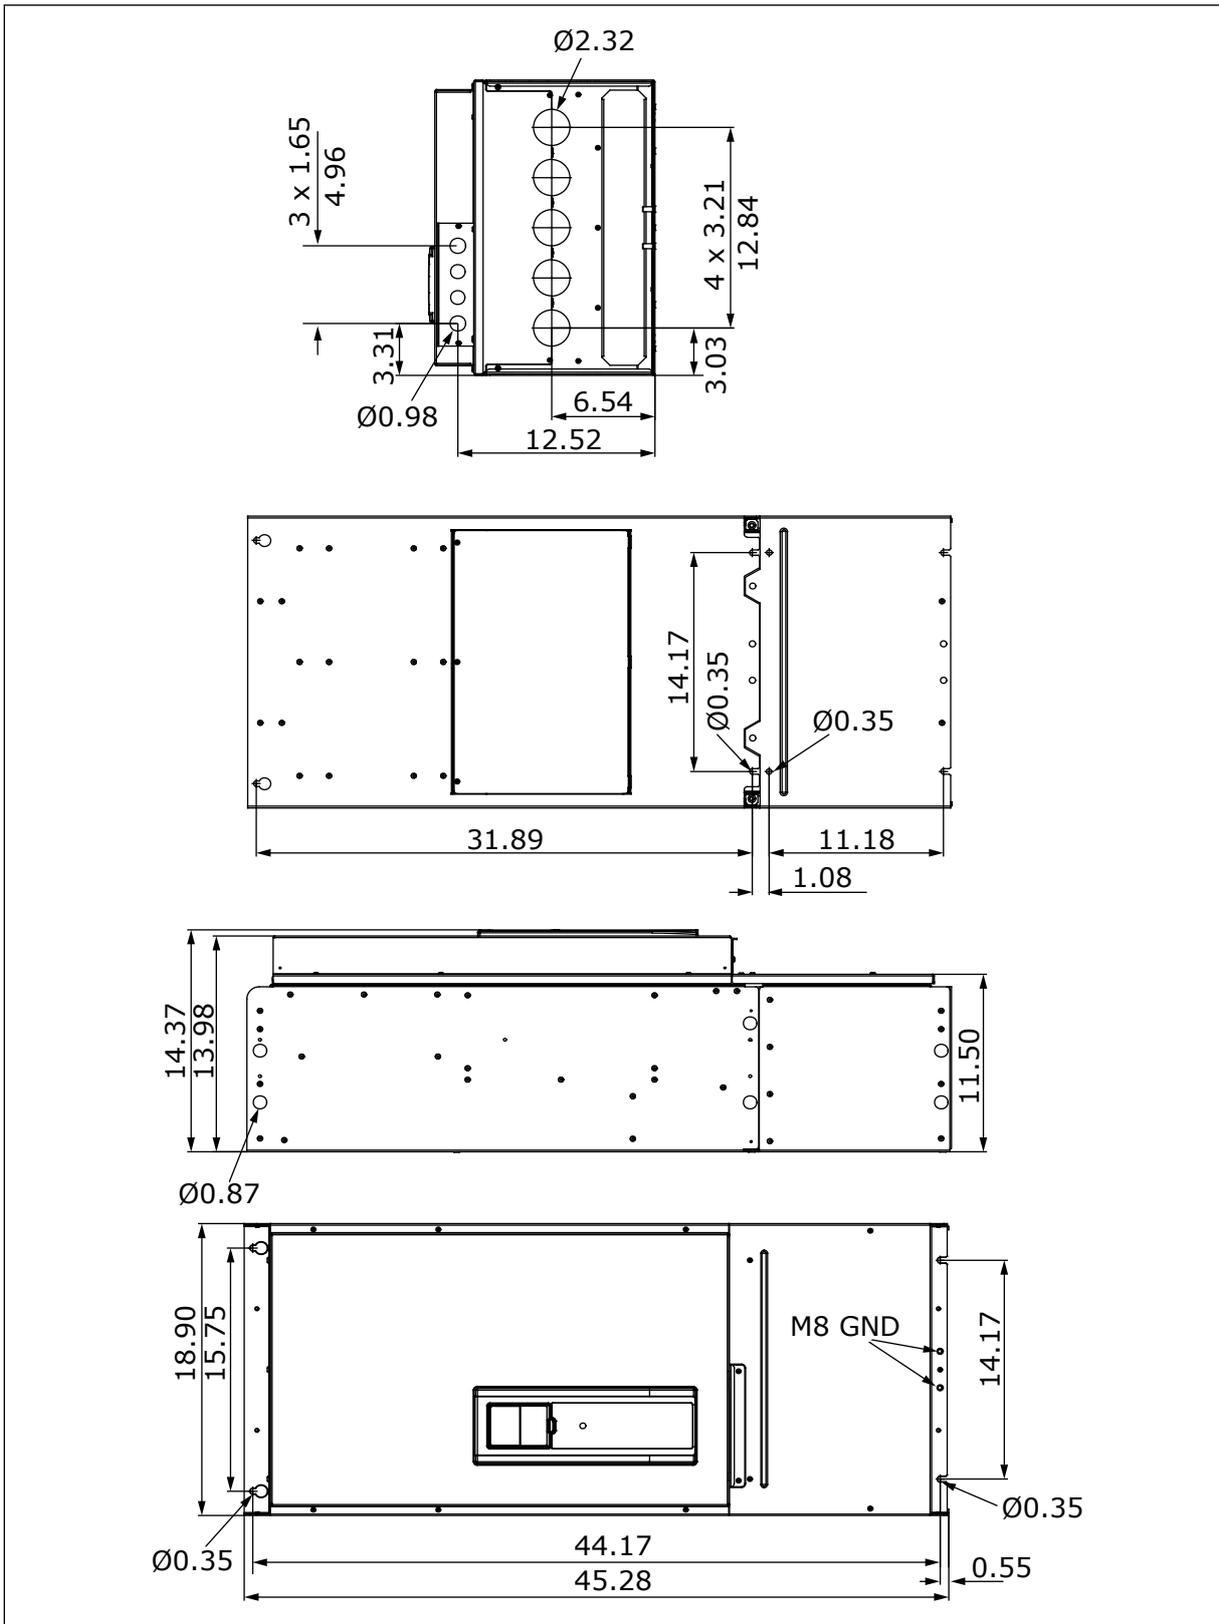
Dimensões do conversor de frequência, MR9 [pol.]
